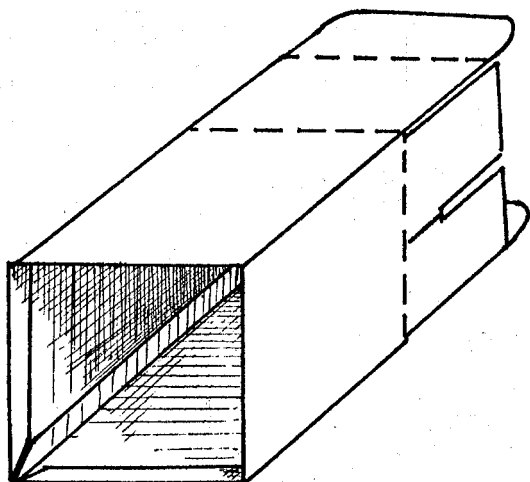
Корпус в сборе с приклеенной отбортовкой
